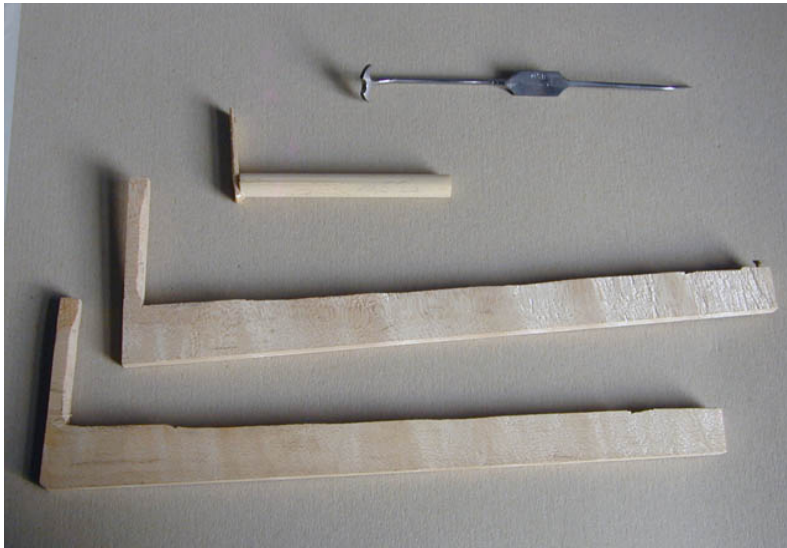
Werkzeuge zum Ein- und Ausbringen der Magnete
